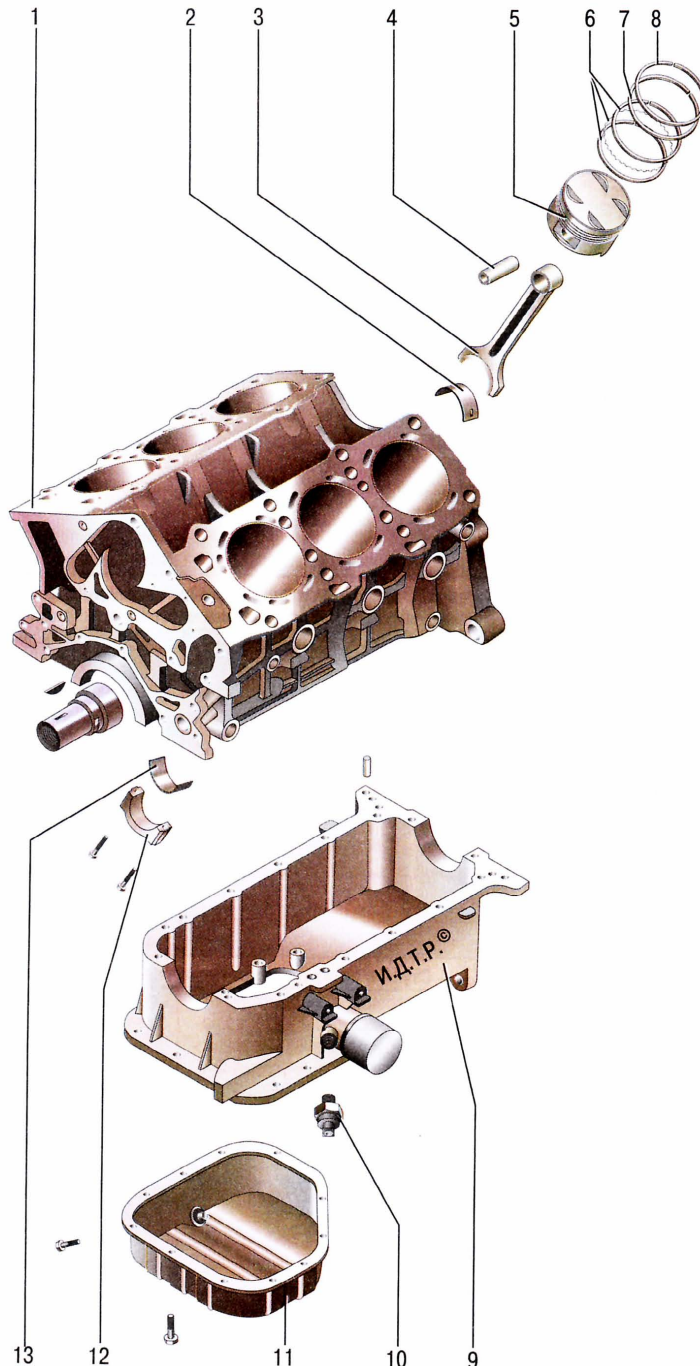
Шатунно-поршневая группа и масляный картер двигателя G6BA: 1 – блок цилиндров; 2, 13 – вкладыши шатунного подшипника; 3 – шатун; 4 – поршневой палец; 5 – поршень; 6 – маслосъемное кольцо; 7 – нижнее компрессионное кольцо; 8 – верхнее компрессионное кольцо; 9 – масляный картер; 10 – датчик сигнала лампы аварийного падения давления масла; 11 – поддон масляного картера; 12 – крышка шатуна
